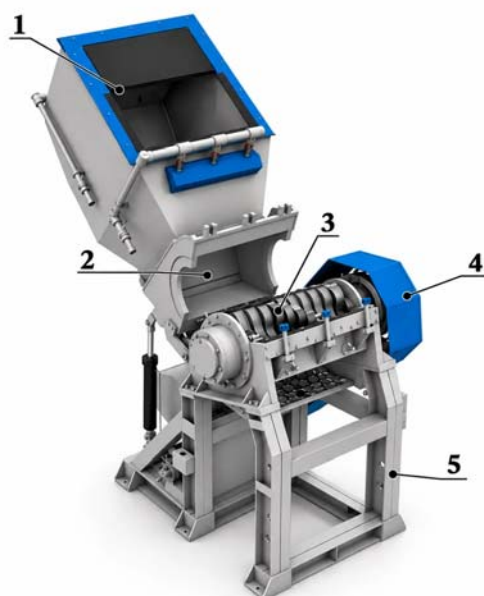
Роторная дробилка: 1 – загрузочный бункер; 2 – корпус; 3 – ротор; 4 – привод; 5 – рама
